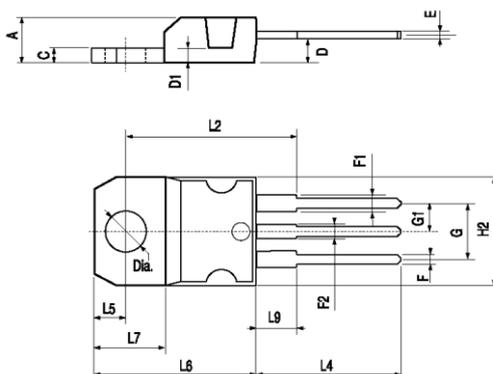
Корпус DA1, VT1-VT4 типа ТО-220
